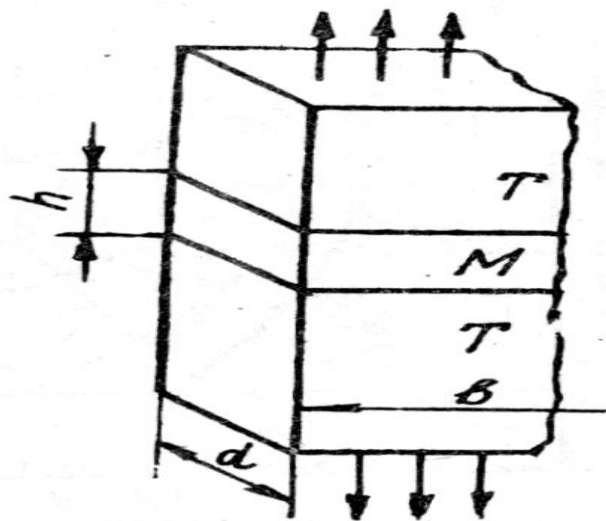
Схема розташування шва поперек розтягального зусилля
